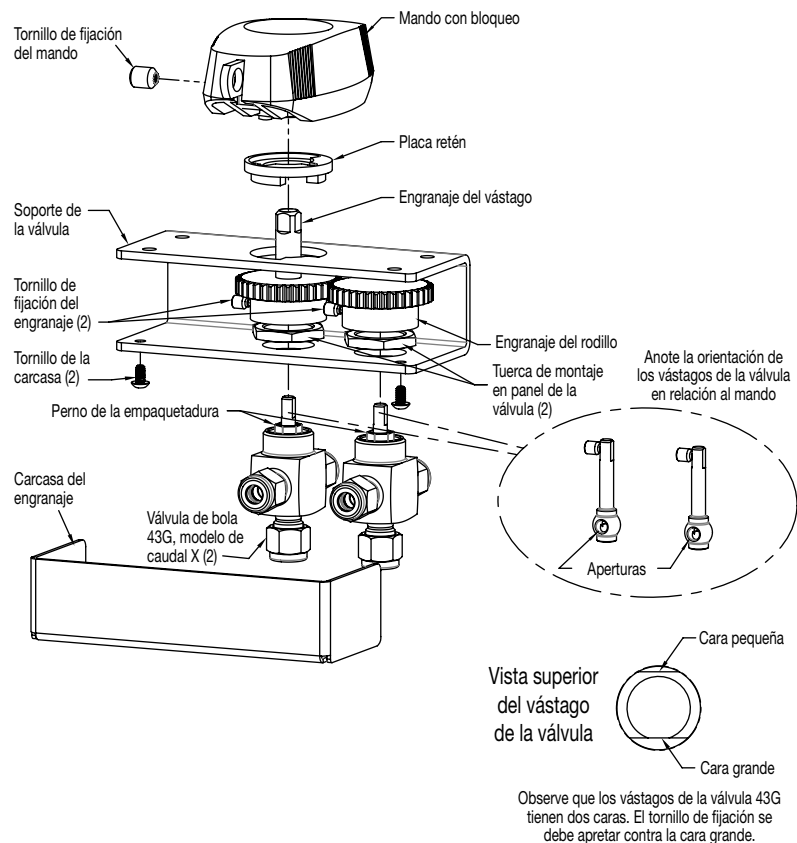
Despiece del ensamble de 2 Válvulas GSM
